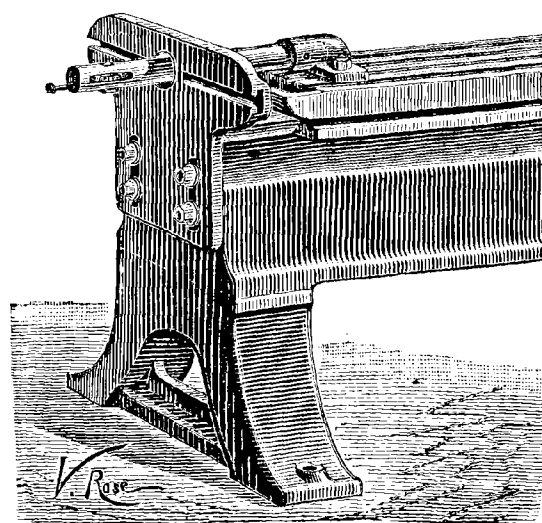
Porte-outil à canneler monté sur une raboteuse.
